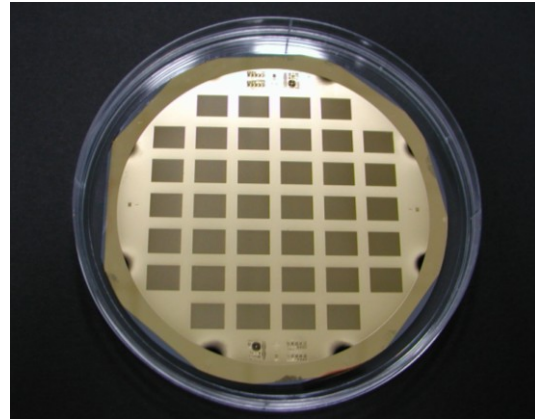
Werkzeugoriginal mit Goldbeschichtung für die Galvanik
